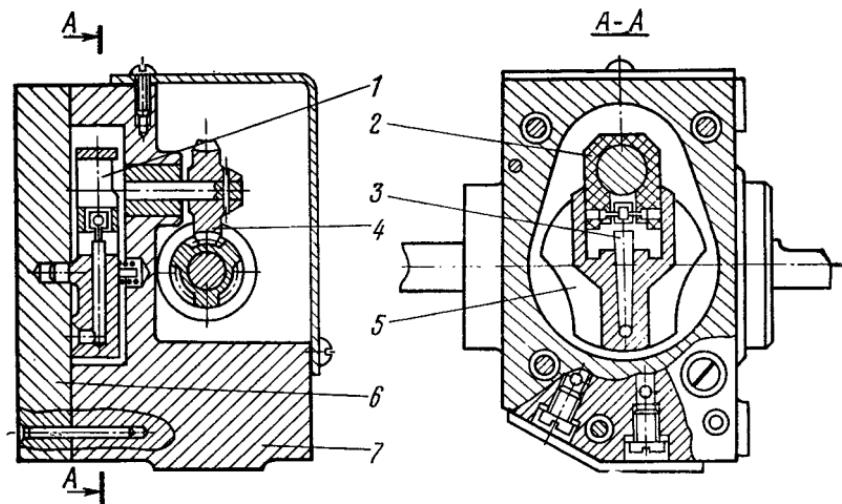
Топливный насос отопительно-вентиляционной установки ОВ-65:
